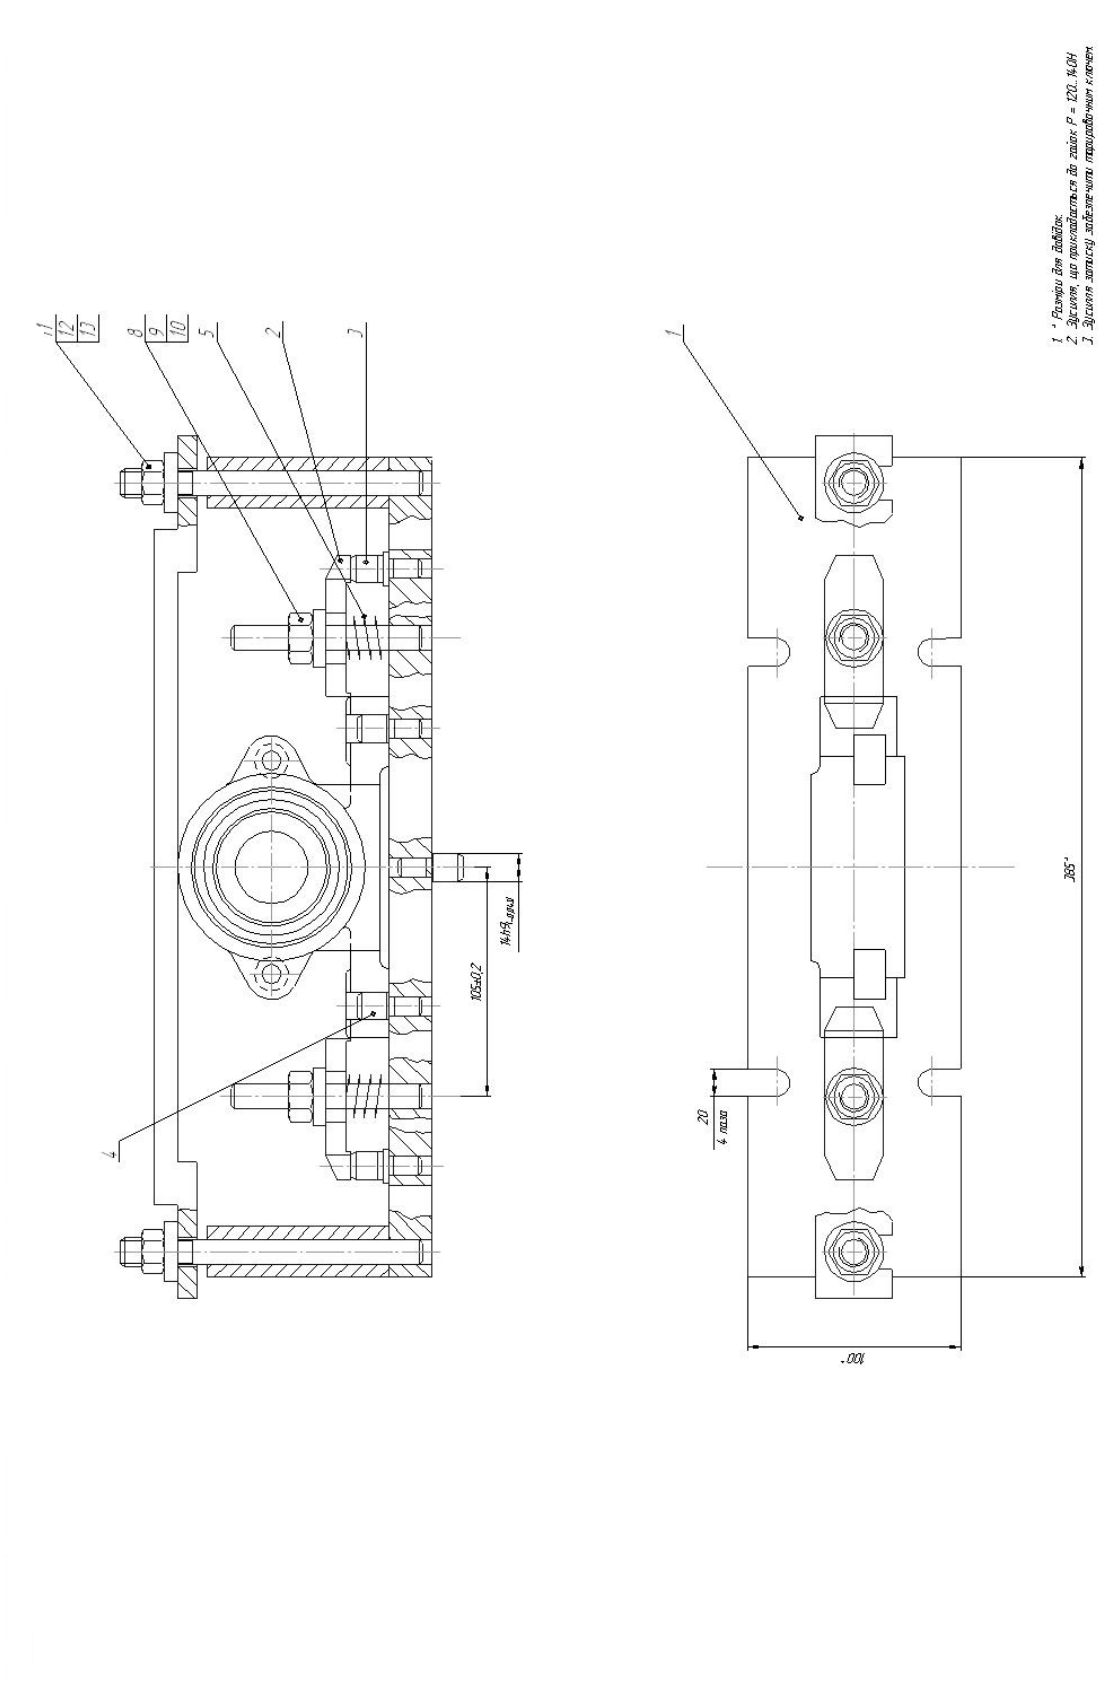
Пристрій для фрезерування торців, розточування, свердління, зенкування, отворів в заготовці «Корпус підшипника» на верстаті з ЧПУ IP500ПМФ4
